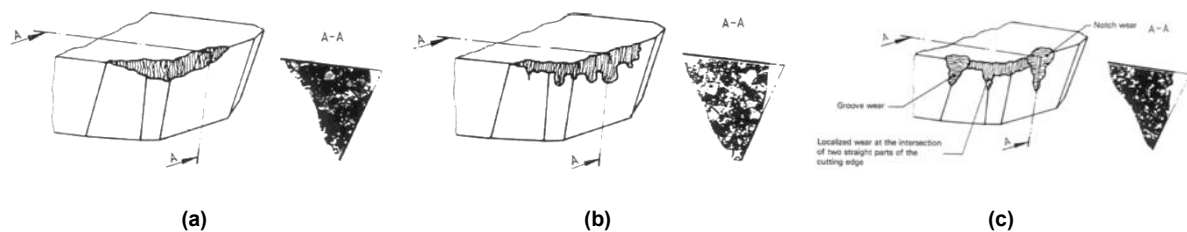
Representação das formas do desgaste de flanco: (a) Uniforme, (b) Não uniforme e (c) Entalhe (ISO-8688-1, 1989)
